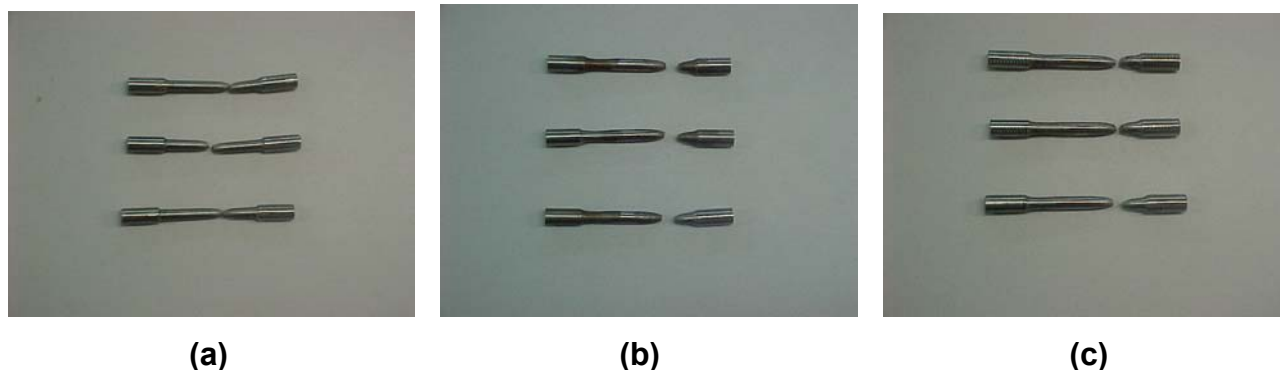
Corpos de prova do ensaio de tração: a) metal base; b) junta soldada procedimento Petrobrás; c) junta soldada hipótese de procedimento
